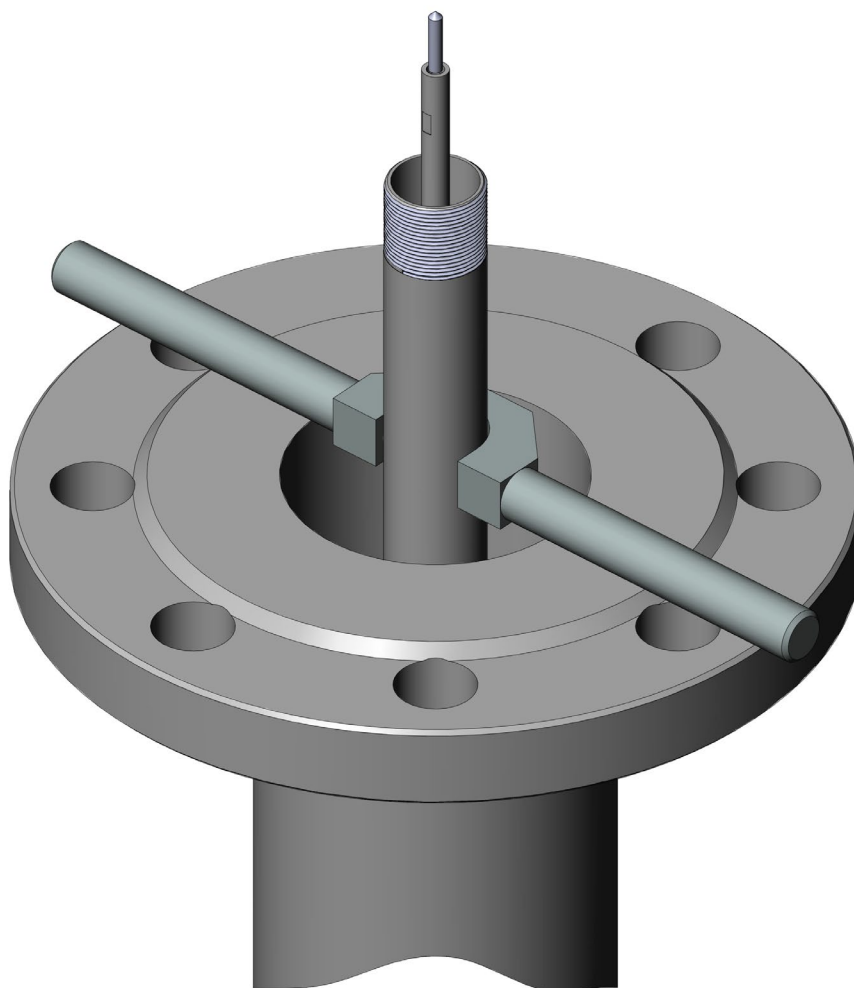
Погружение верхней секции в резервуар с опорой на верхнее приспособление
